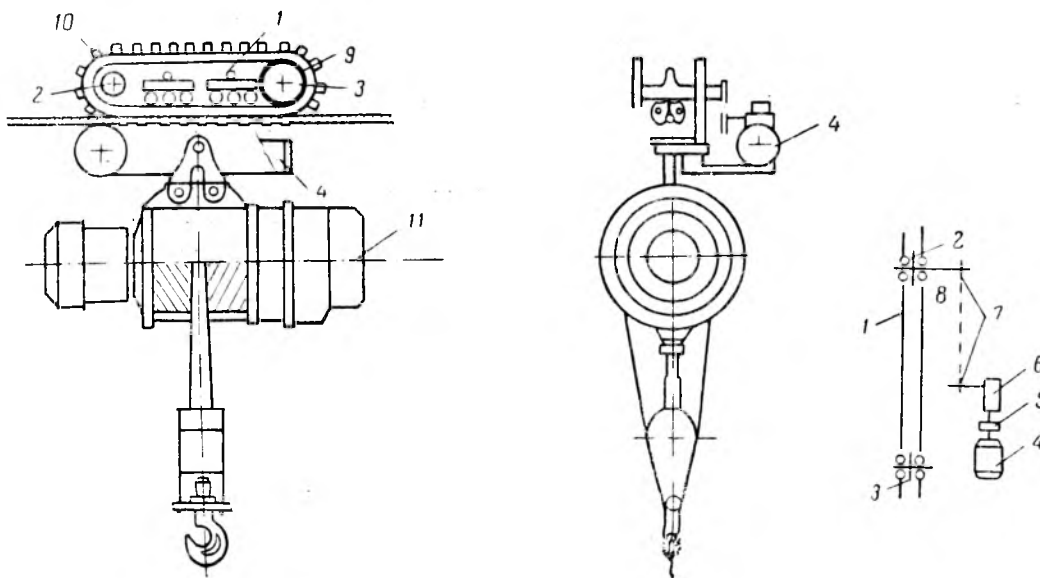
Общий вид СТЭЛ: 1 — балансирная подвеска; 2 — направляющая звездочка; 3 — ведущая звездочка; 4 — тяговый электродвигатель; 5 — муфта сцепления; 6 — редуктор; 7 — звездочки цепной передачи; 8 — цепь передаточная; 9 — гусеничная тяговая цепь; 10 — тросозахватные рычажки; 11 — тельфер стандартный
